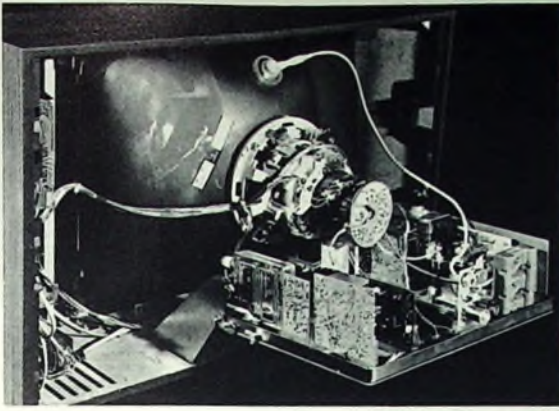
Mit Modulen bestückte ausgeschwenkte Grundplatte
